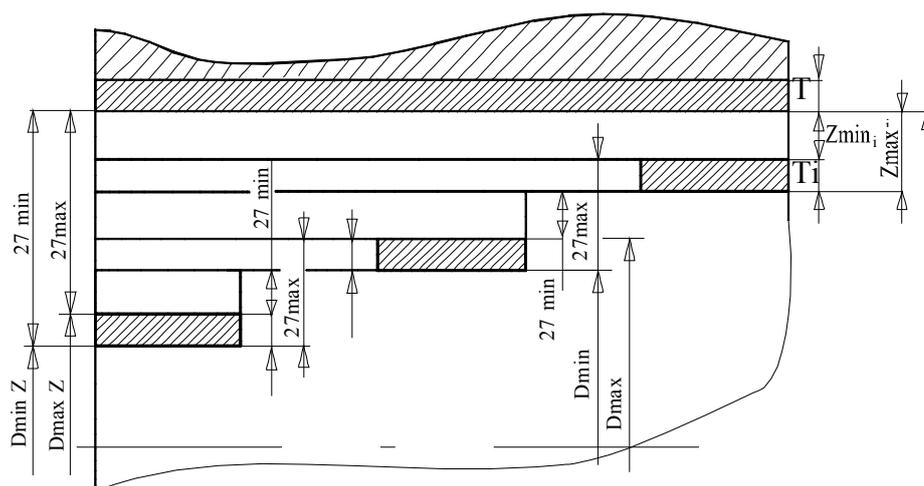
Схема связей между межпереходными размерами, припусками и допусками для охватывающих поверхностей
